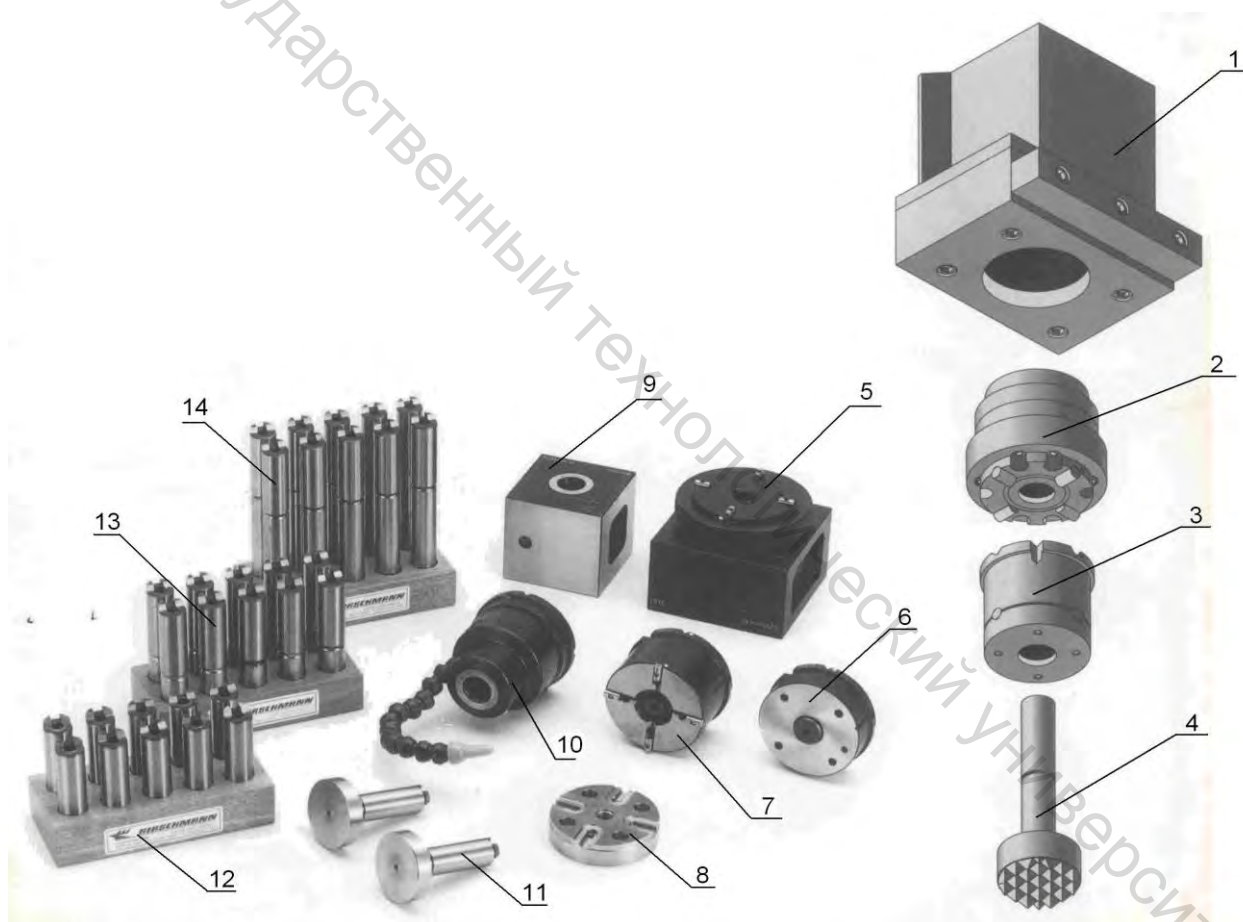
Инструментальная оснастка станков для объемного копирования и пример ее использования: 1 – ползун станка, 2 – шпиндель, 3 – патрон (цанговый, пневматический или электромагнитный), 4 – электрод-инструмент, 5 – автоматический патрон, 6, 7, 8 – сменные планшайбы для патрона, 9 – держатель для электрода-инструмента, 10 – сменная планшайба с оправкой для промывки, 11 – держатель электрода-инструмента, 12, 13, 14 – хвостовики для изготовления электродов-инструментов
